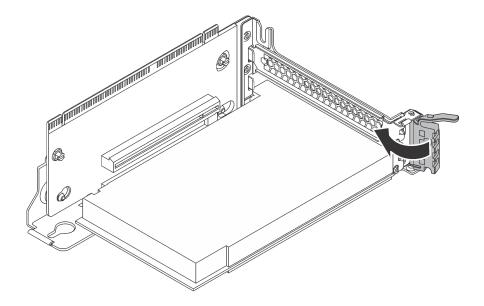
Cierre del mecanismo de cierre de sujeción del adaptador PCIe
